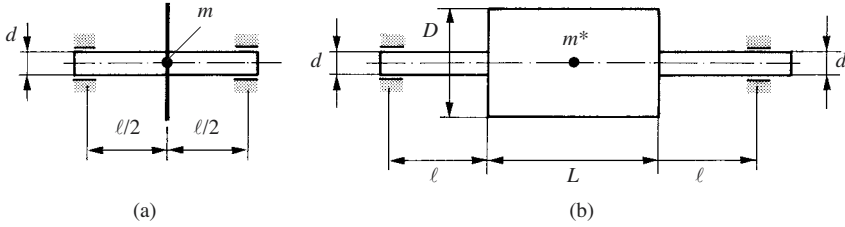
Rotors: (a) disque plat au milieu de la portée; (b) rotor réel symétrique.
